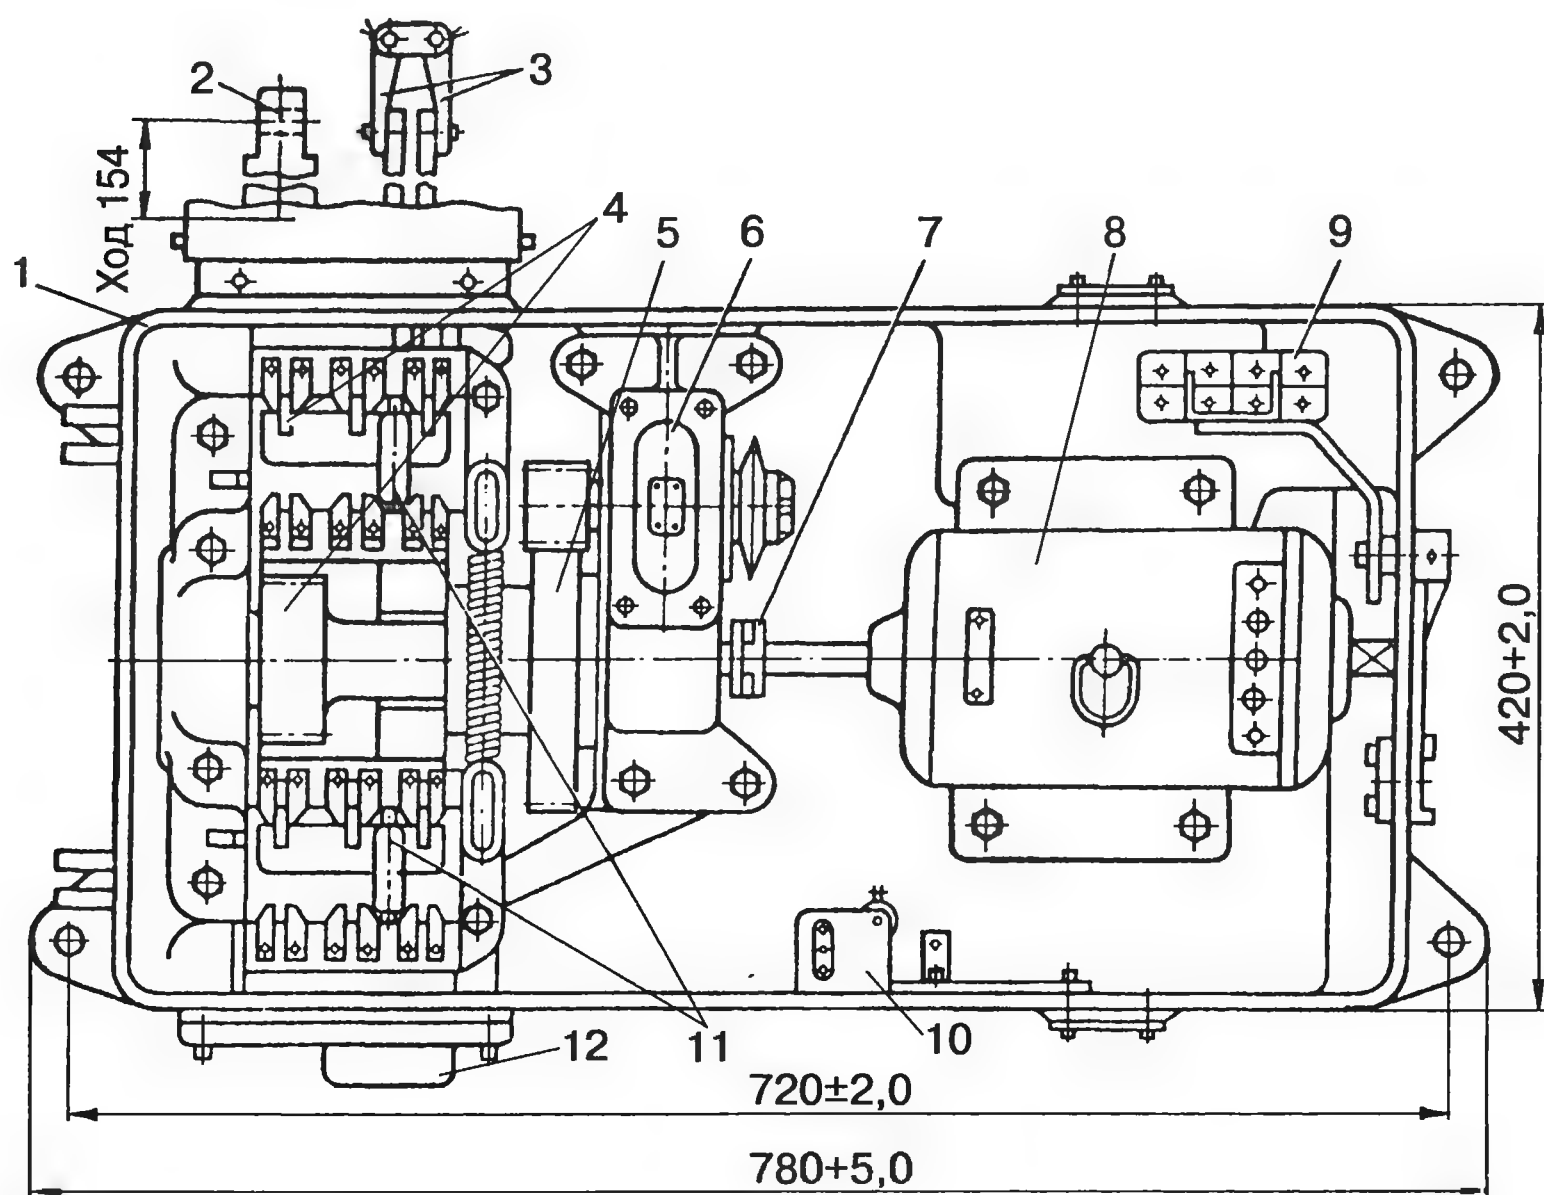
Электропривод стрелочный типа СП-6 (вид сверху)
